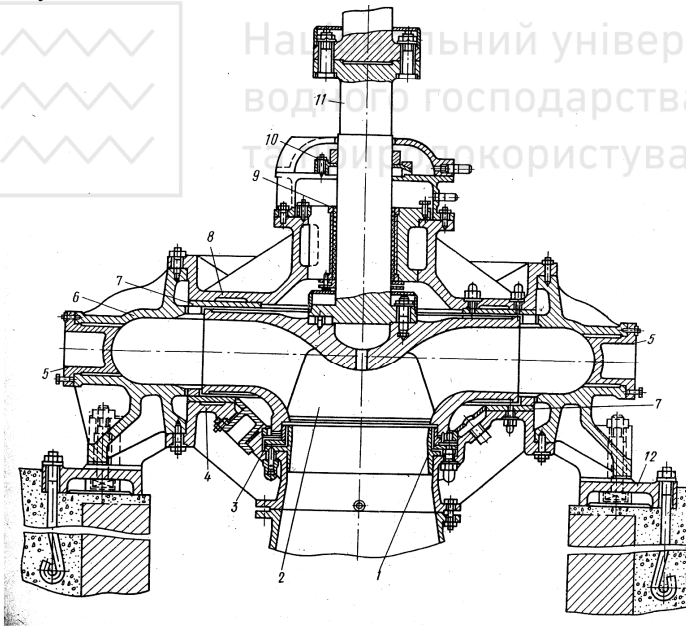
Насос типу СДВ: 1-захисне кільце; 2- робоче колесо; 3- регульоване ущільнююче кільце; 4- нижня кришка корпусу; 5- люк для очищення насоса; 6- корпус; 7- захисні диски; 8- верхня кришка корпусу; 9- підшипник ковзання; 10- торцеве ущільнення вала; 11- вал; 12- фундаментна плита
